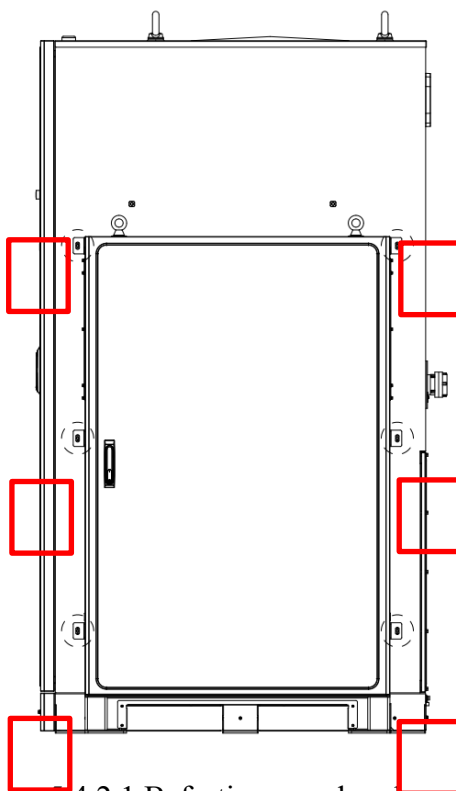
Befestigungsschrauben anbringen
